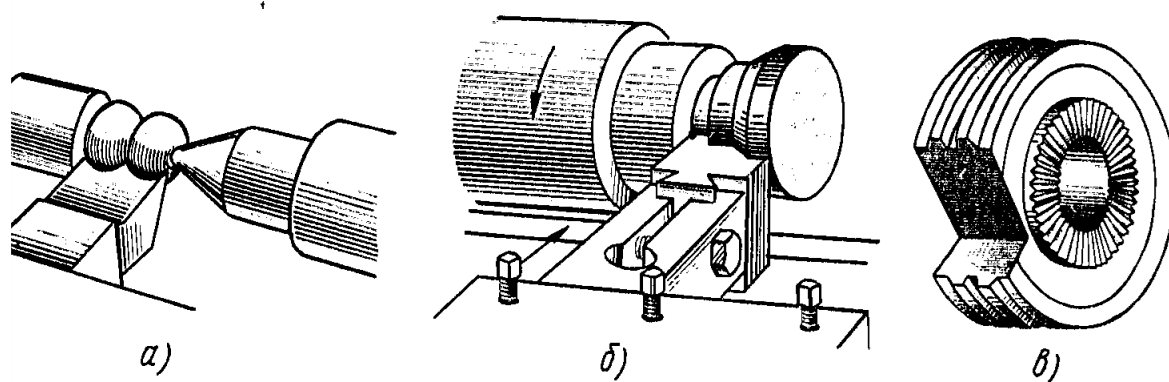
Фасонные резцы: а – цельный; б – сборный; в – дисковой
